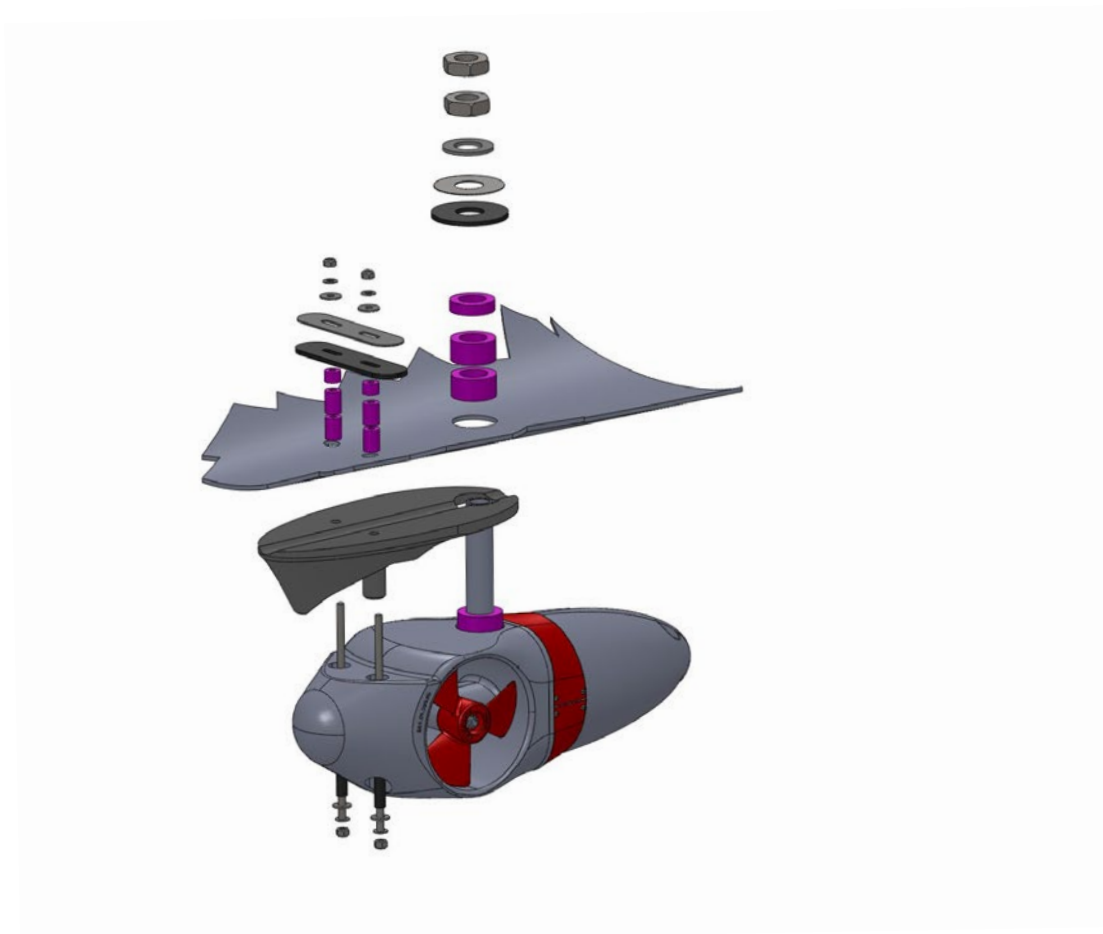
Monteringssett "Adapter" på stål og aluminium
